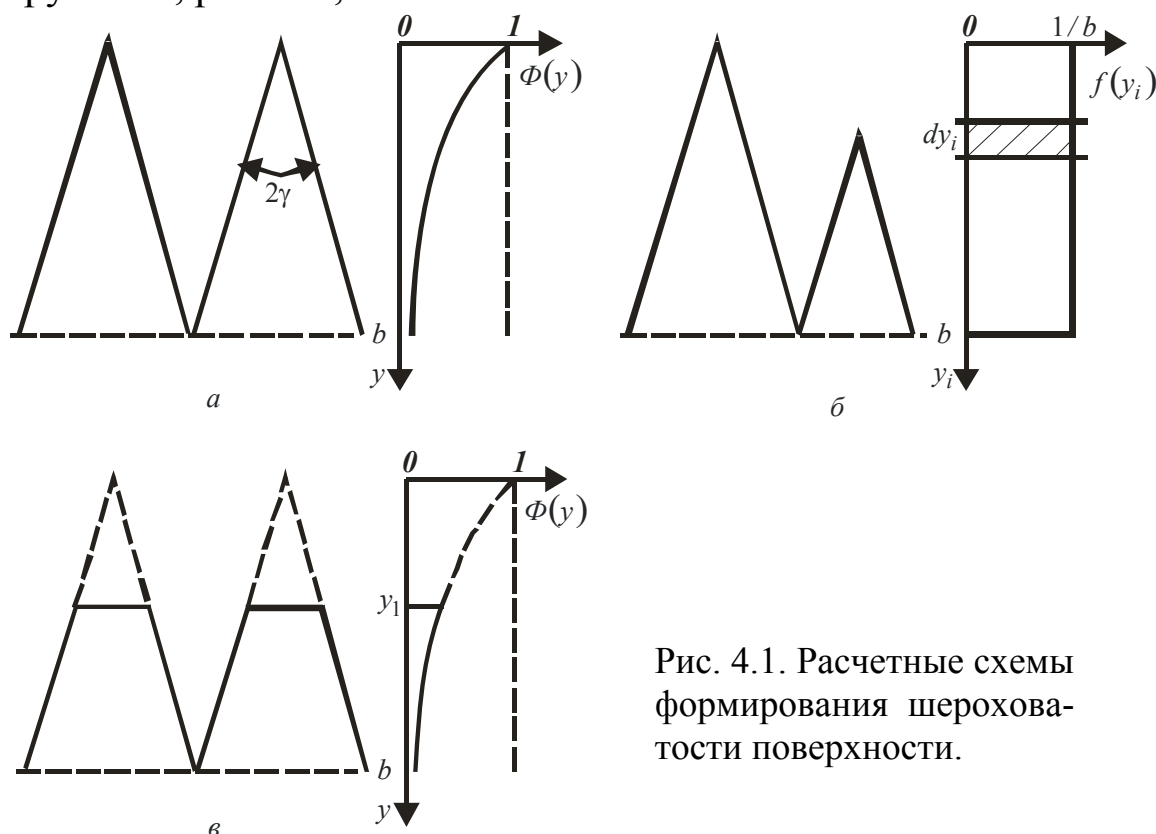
Расчетные схемы формирования шероховатости поверхности.
